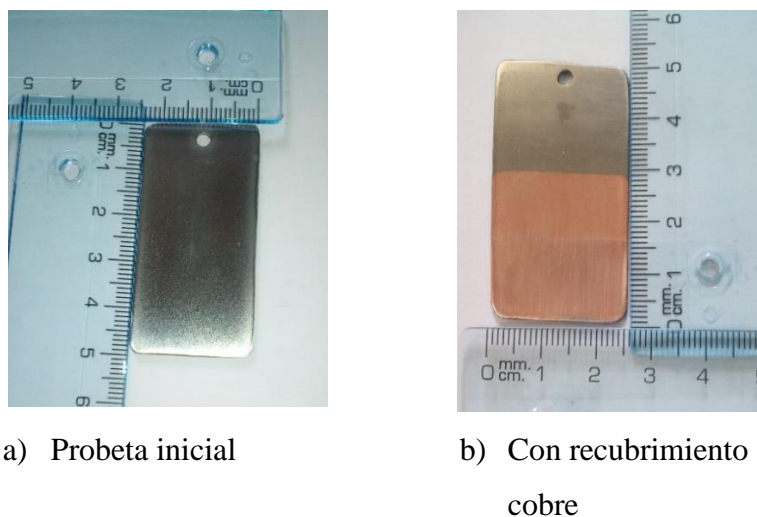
Dimensiones de probetas utilizadas en las pruebas
